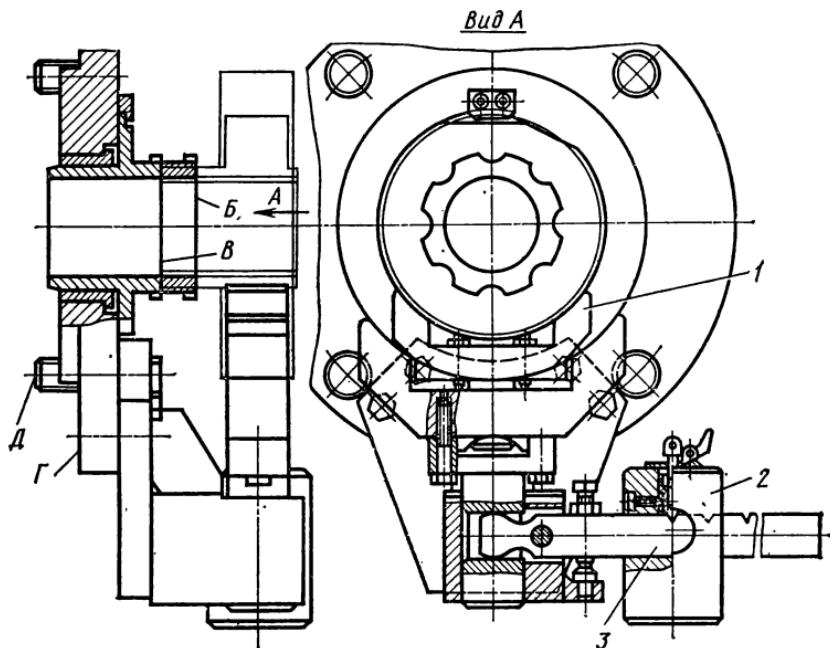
Протяжное приспособление с уравновешивающим грузом:
